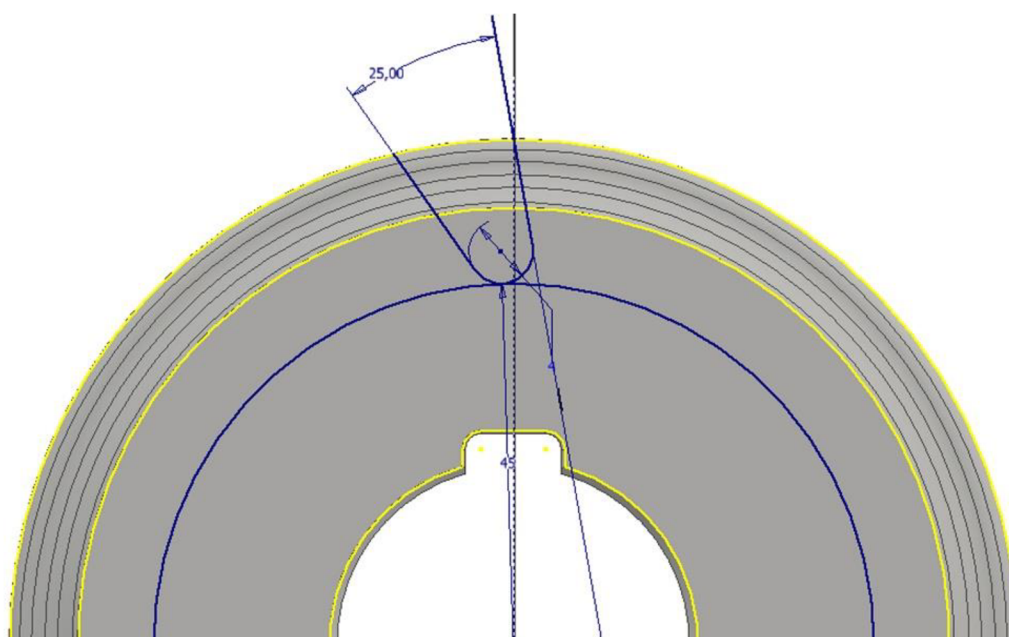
Rotace geometrie podél základní osy nástroje.
